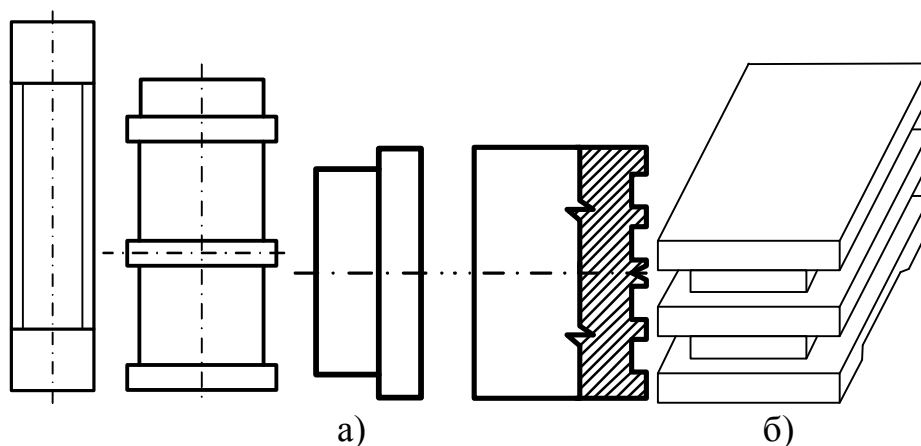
Образцы изделия для проверки точности МРС:
